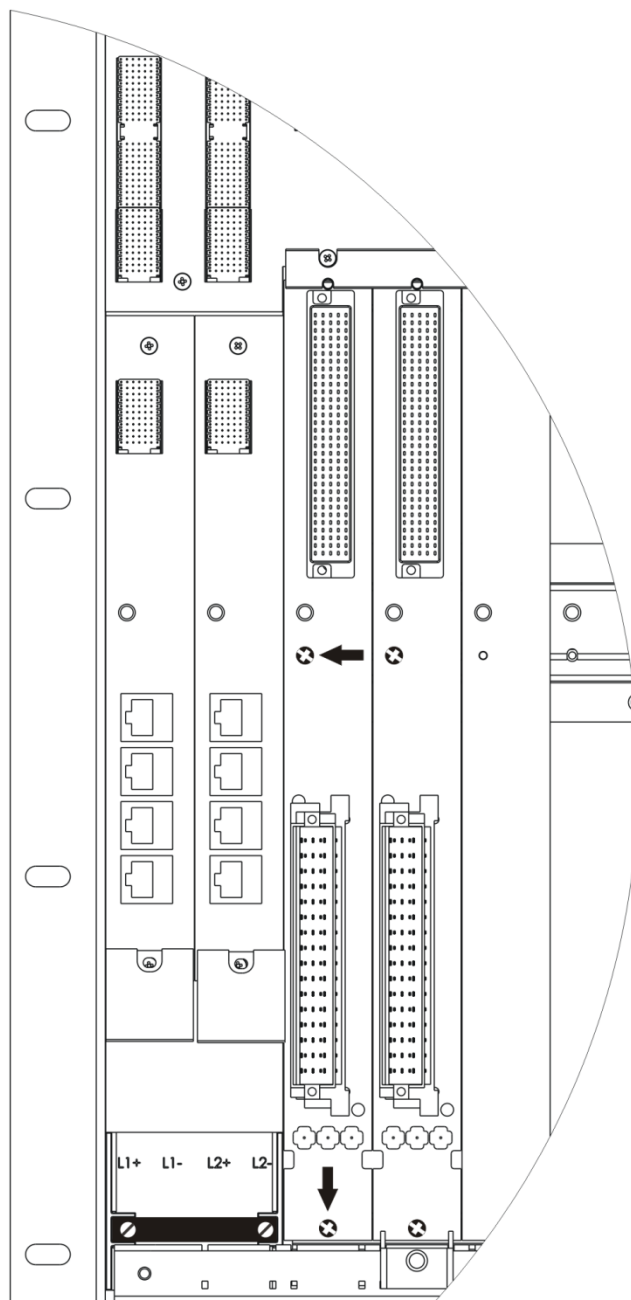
Festschrauben des Mono Connector Boards, exemplarisch
